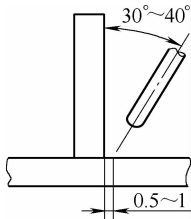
斜角焊的焊丝与工件的位置示意
